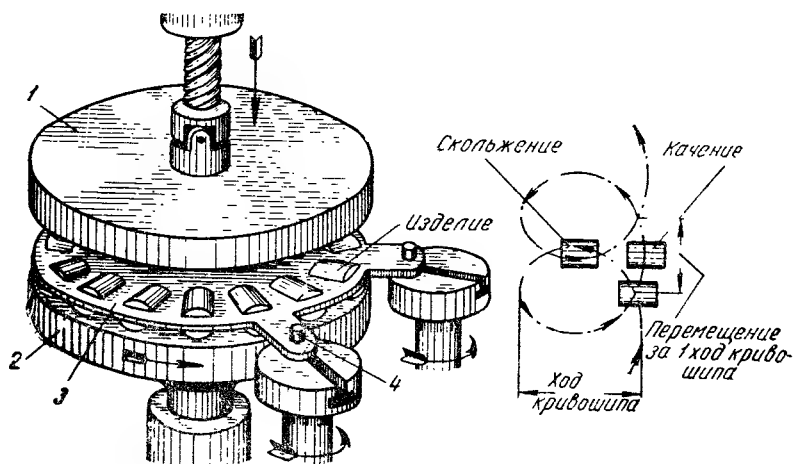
Доводочная бабка для цилиндрических деталей:
